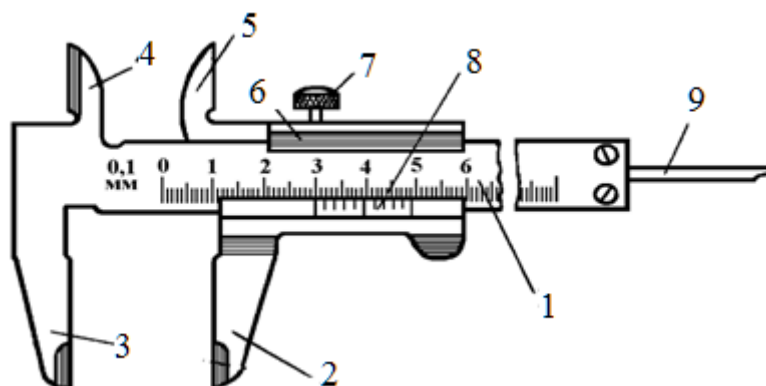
Штангенциркуль ШЦ-I: 1 – штанга; 2 – подвижная нижняя ножка; 3 – неподвижная нижняя ножка; 4 – неподвижная верхняя ножка; 5 – подвижная верхняя ножка; 6 – рамка; 7 – винт для зажима рамки; 8 – нониус; 9 – линейка глубиномера
